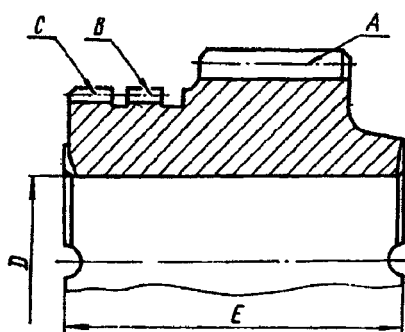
Колесо зубчатое первой передачи промежуточного вала
